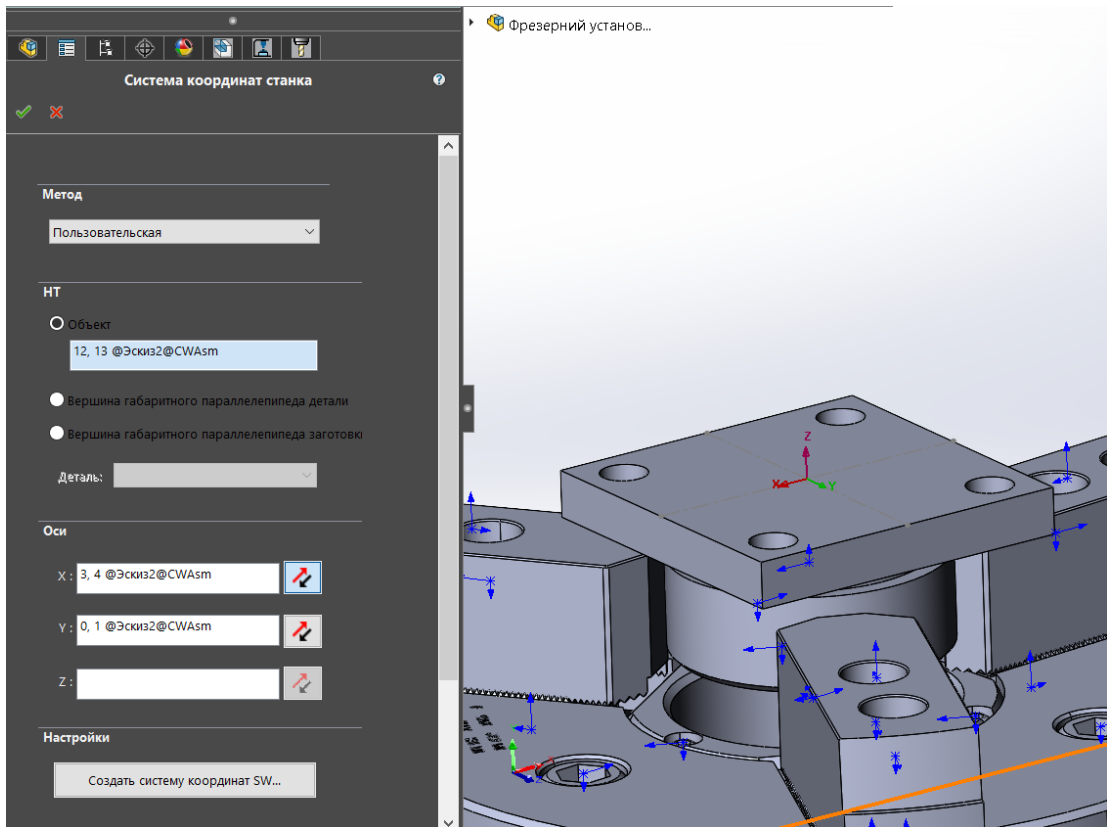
Встановлення системи координат фрезерного верстата
